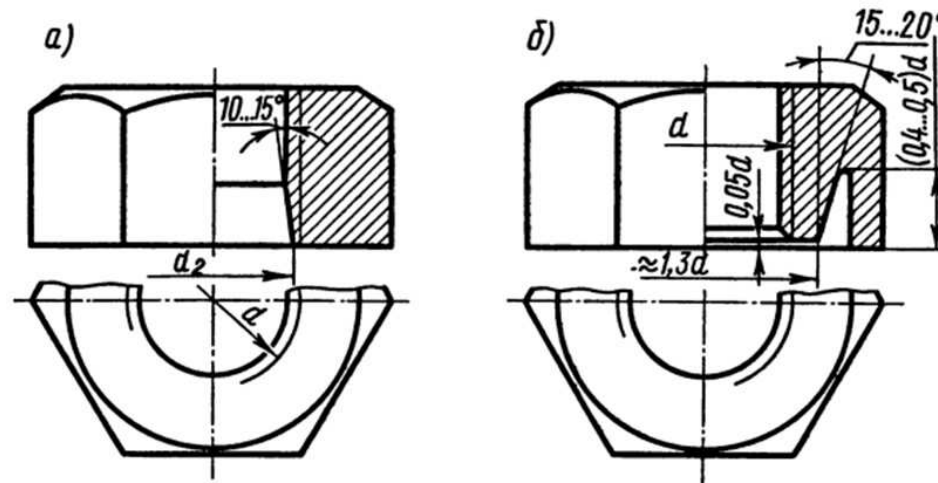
Конструкции гаек для выравнивания сил по виткам резьбы:
